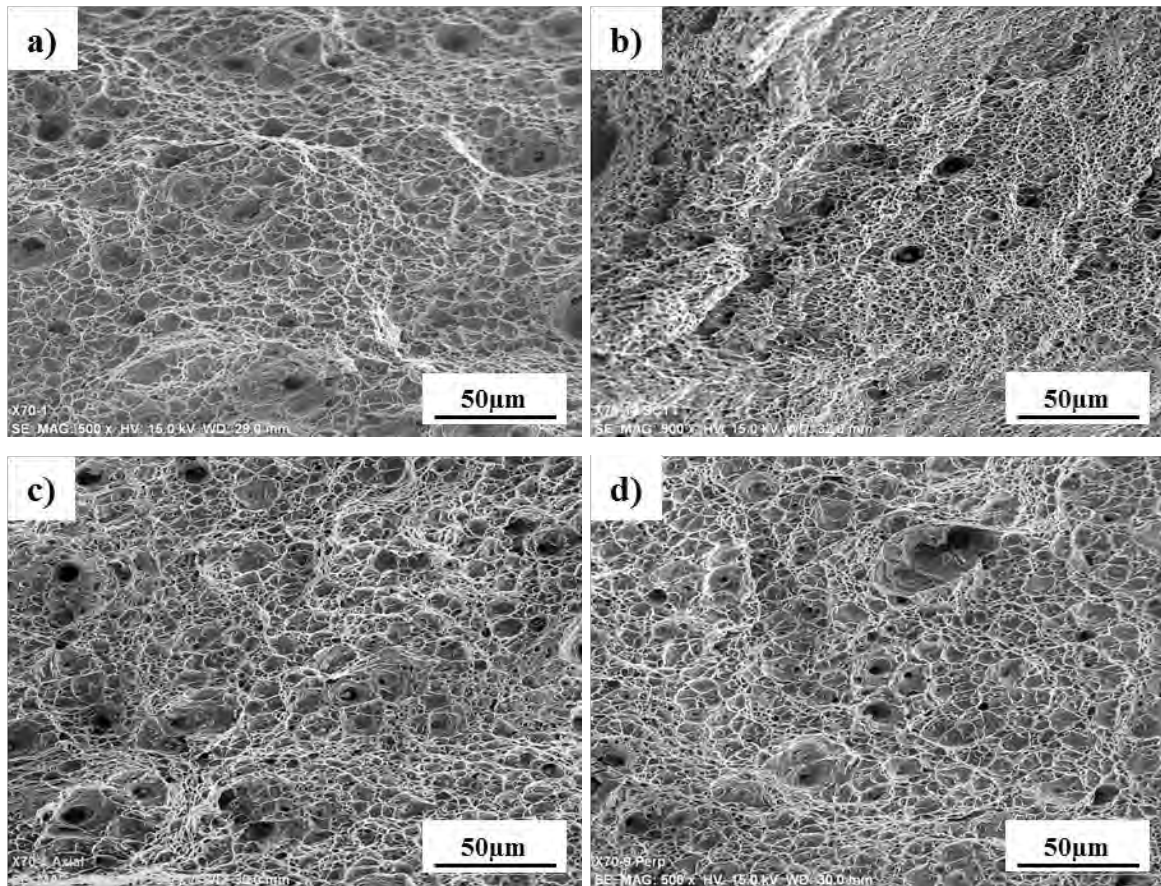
Imágenes obtenidas por MEB de las superficies de fractura de las probetas de tensión de las soldaduras del acero API X-70; a) sin CM, b) sin CM y placas con TT, c) con CMA y d) con CMP.
